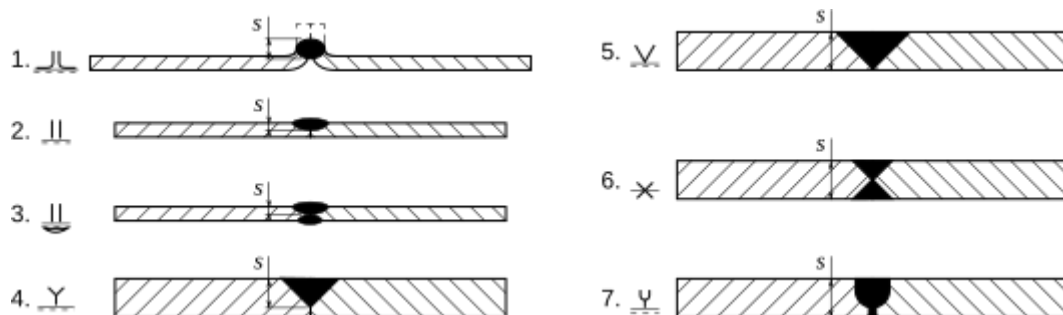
Symboles élémentaire soudure bout a bout
